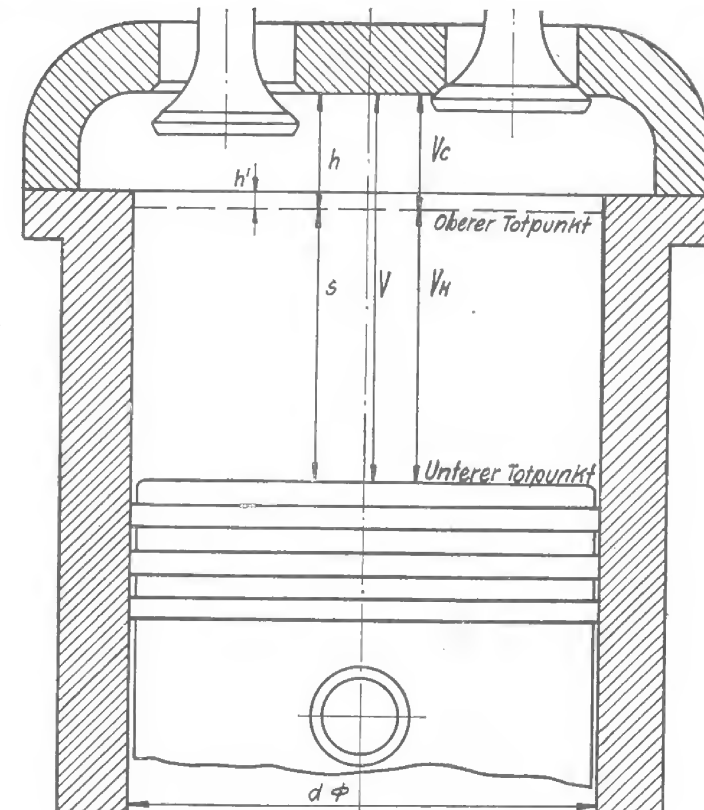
Erklärungen hierzu in nachstehender Tabelle
